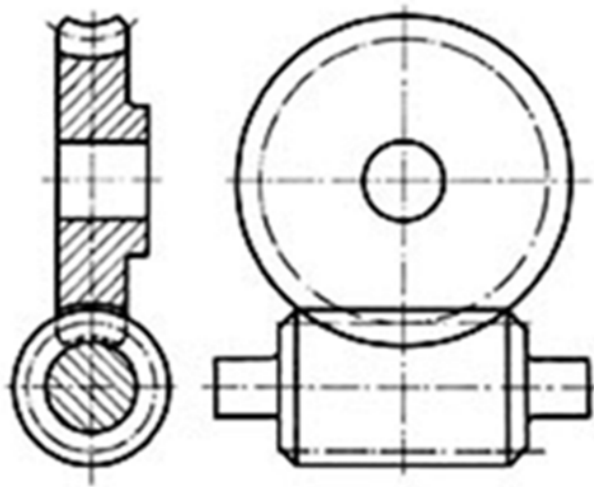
Engranes de tornillo sin fin y rueda helicoidal de transmisión de movimiento circular
